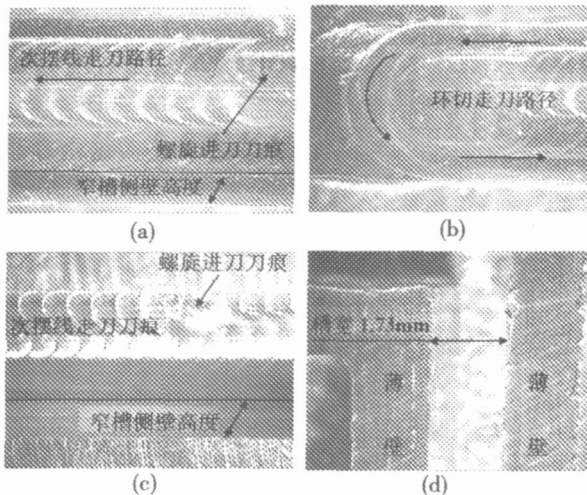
1 mm 立铣刀铣削宽 4.175 mm 槽局部形貌 20 ×
